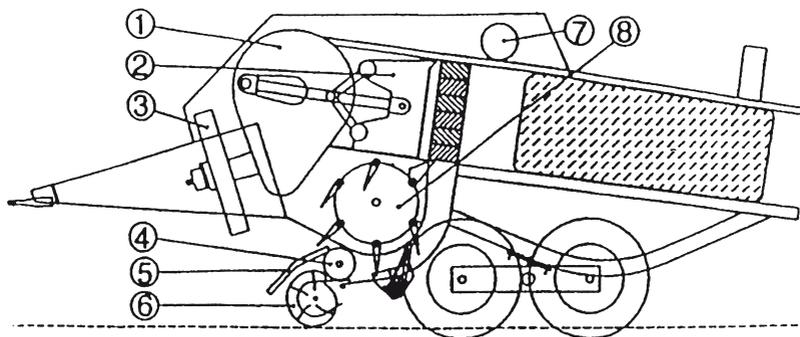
Схема устройства пресс-подборщика высокого давления, формирующего малогабаритные тюки (428, 648)
